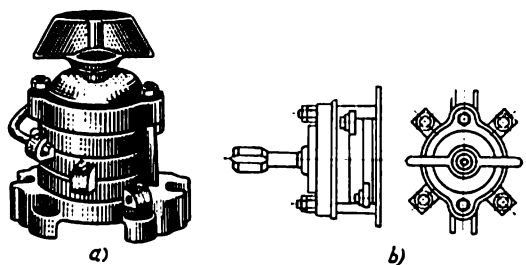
Interrupteur rotatif (*a* — vue d'ensemble; *b* — schéma)
